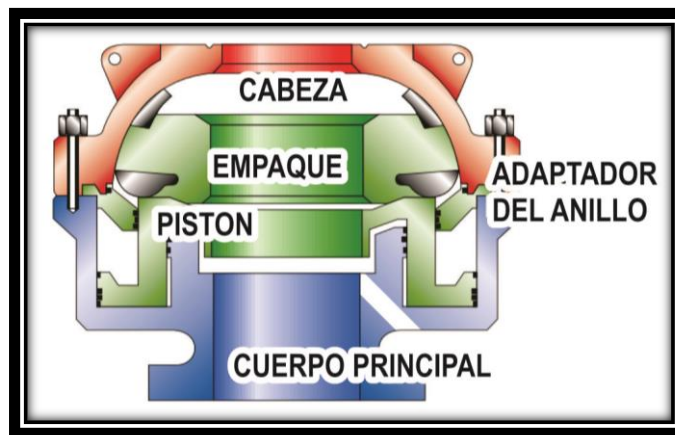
Partes del preventor Shaffer – Cabeza esférica
